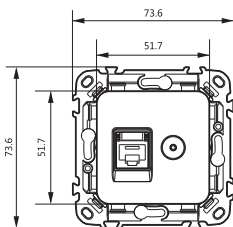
Габаритные и установочные размеры розеток (лист 1 из 4) / Figure 2 – Overall and installation dimensions of sockets (sheet 1 of 4) / 2-сурет – Розеткалардың жалпы және орнату өлшемдері (4-ден 1-парақ)
